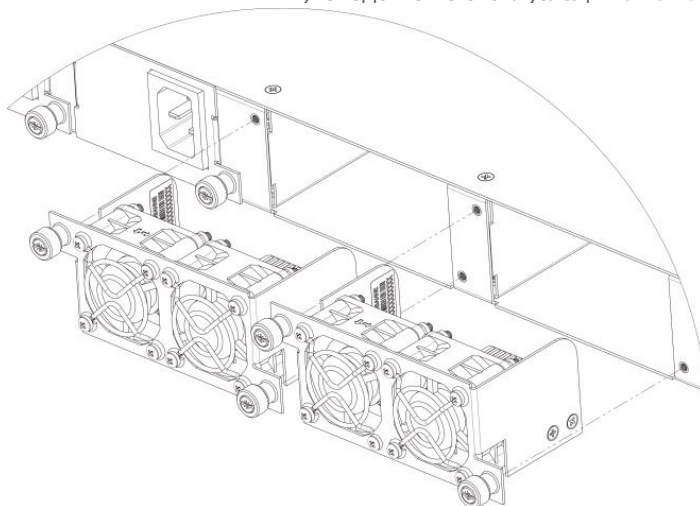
Блок вентиляции SMG-3016. Крепление в корпус
